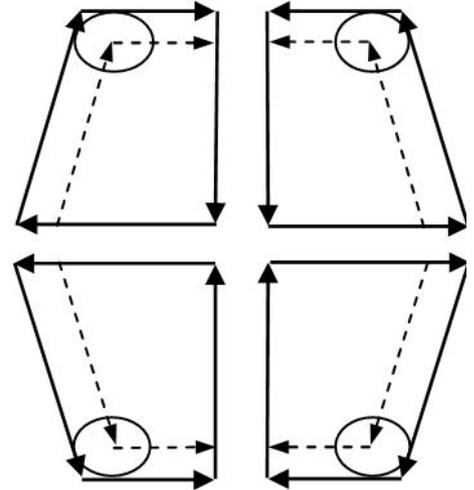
Направление коррекции на радиус закругления режущей кромки инструмента в команде G94
